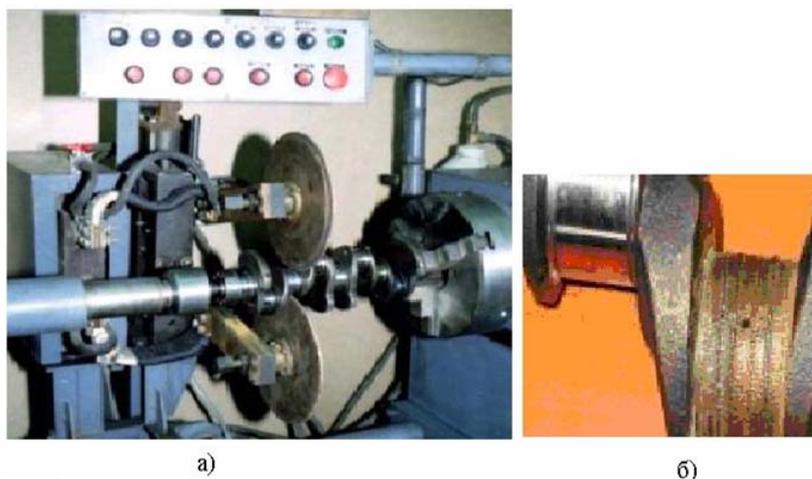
Процесс электроконтактной наварки шейки коленчатого вала:
